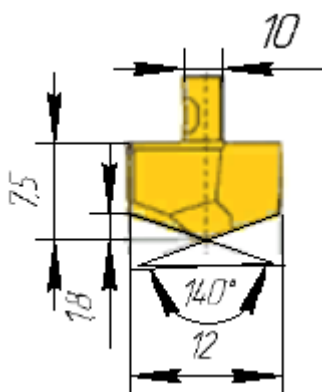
Головка для сверления 870-1200-10-PM
